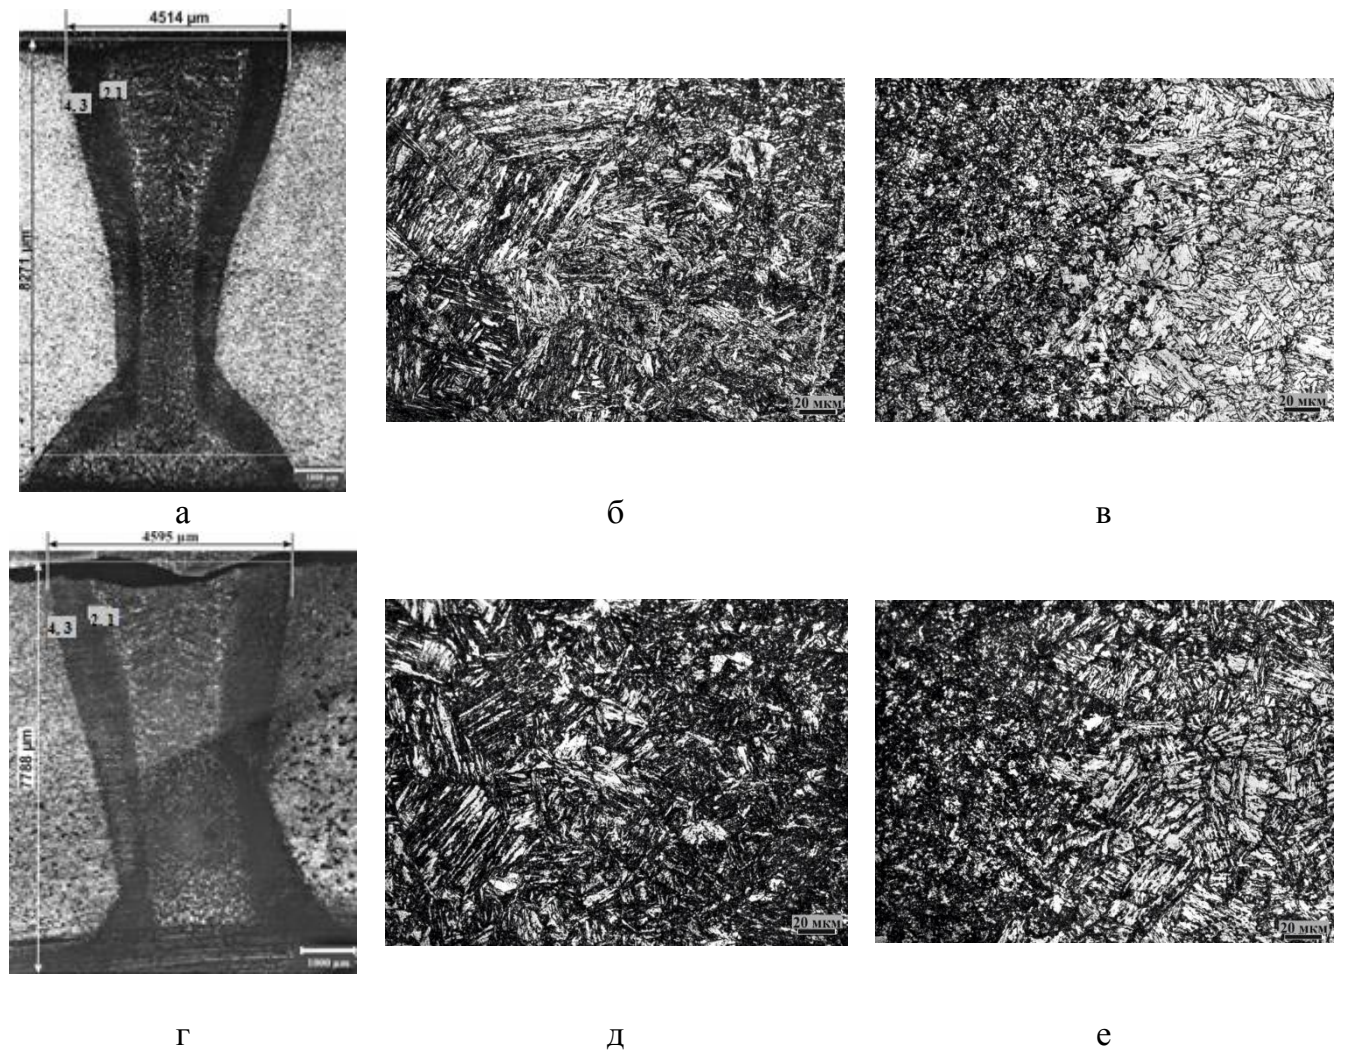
Структура ЗТВ сварных стыковых соединений, полученных лазерной сваркой с погонной энергией 3,3 кДж/см без предварительного подогрева (а-в) и с предварительным подогревом 100<sup>0</sup>С (г-е) [123], где:
